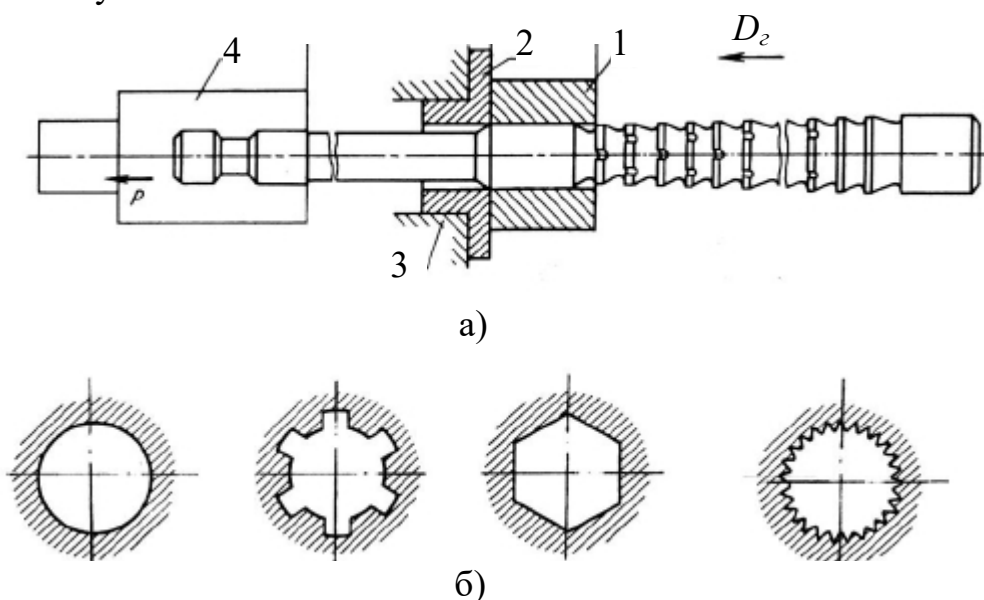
Схема протягування (а) та форми протягнутих отворів (б): 1 – заготовка; 2, 3 – пристосування; 4 – виконавчий елемент верстата
